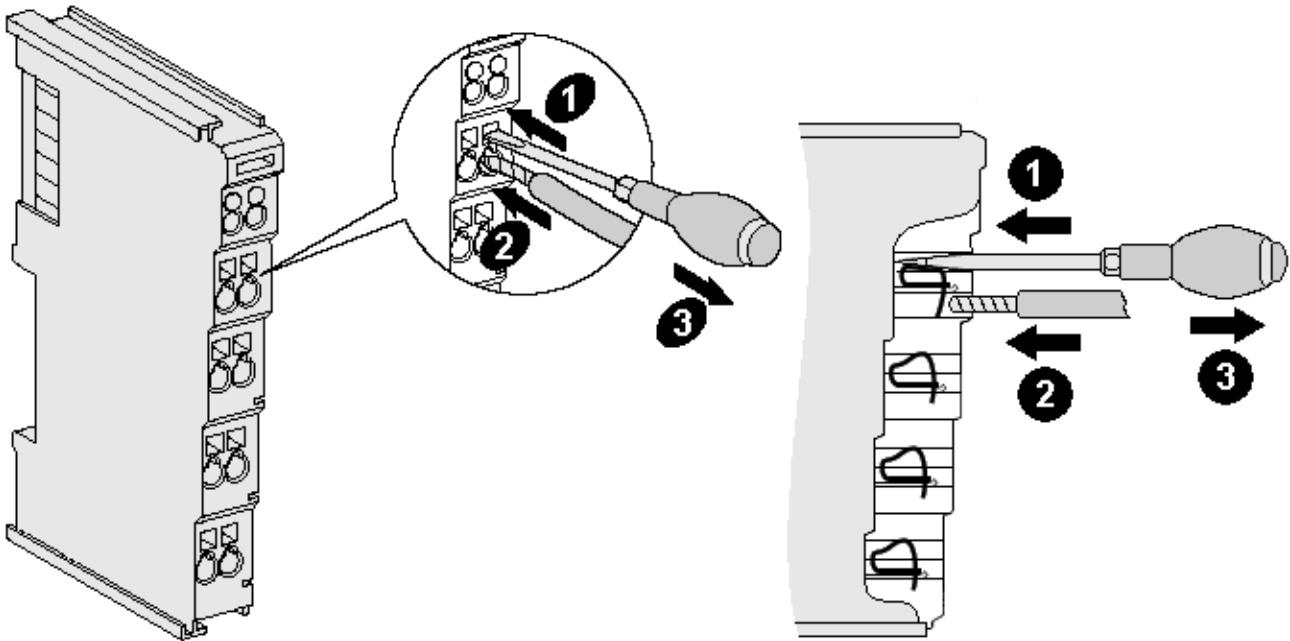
Anschluss einer Leitung an eine Klemmstelle
